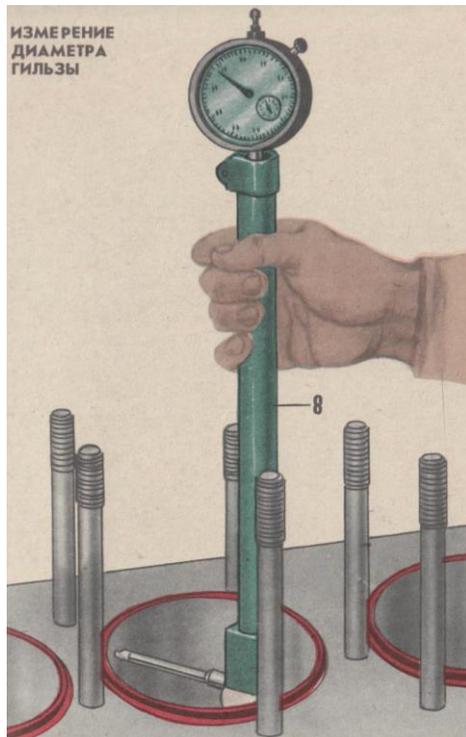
Схема измерения диаметра цилиндра блока двигателя
